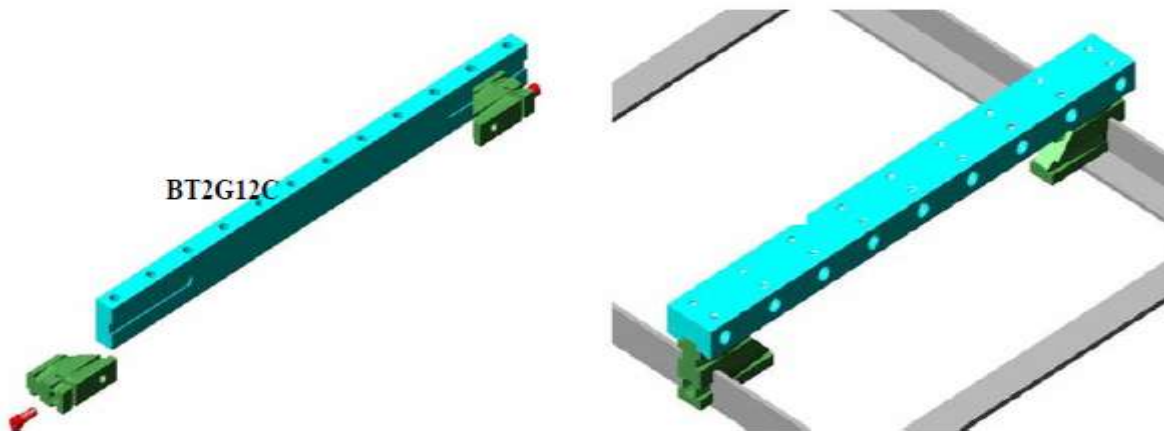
Barras de acero galvanizado BT2G12C con aisladores deslizables.
